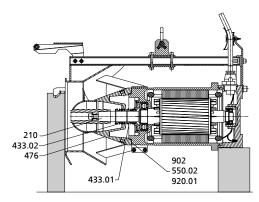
Montaje del cierre mecánico en Amaline 300 con motor 86
